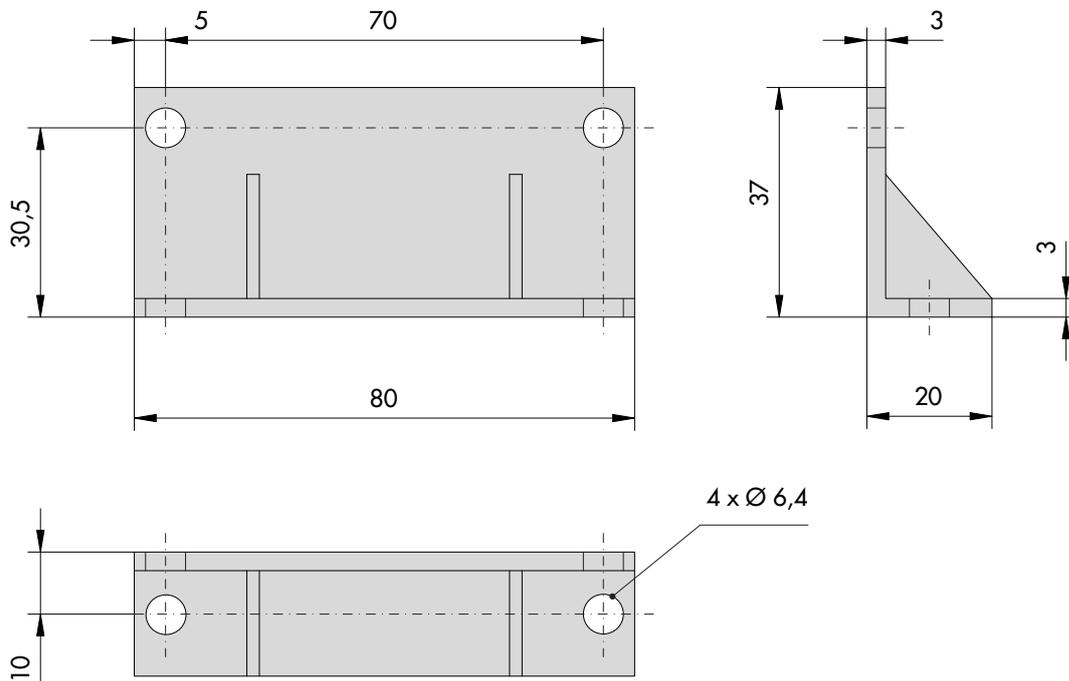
unidad de montaje, montada con el SE 200, en un tubo de medición.
